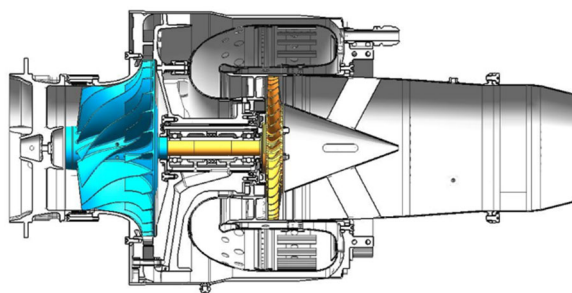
Конструктивная схема малоразмерного газотурбинного двигателя
